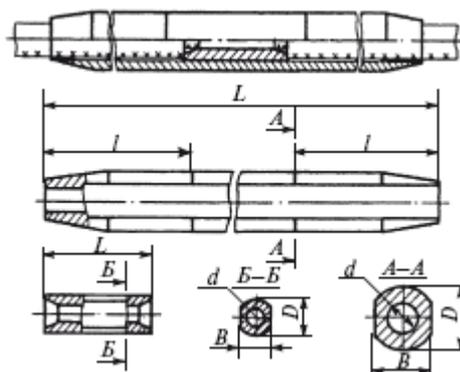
Соединительный прессуемый зажим типа САС для сталеалюминиевых проводов
